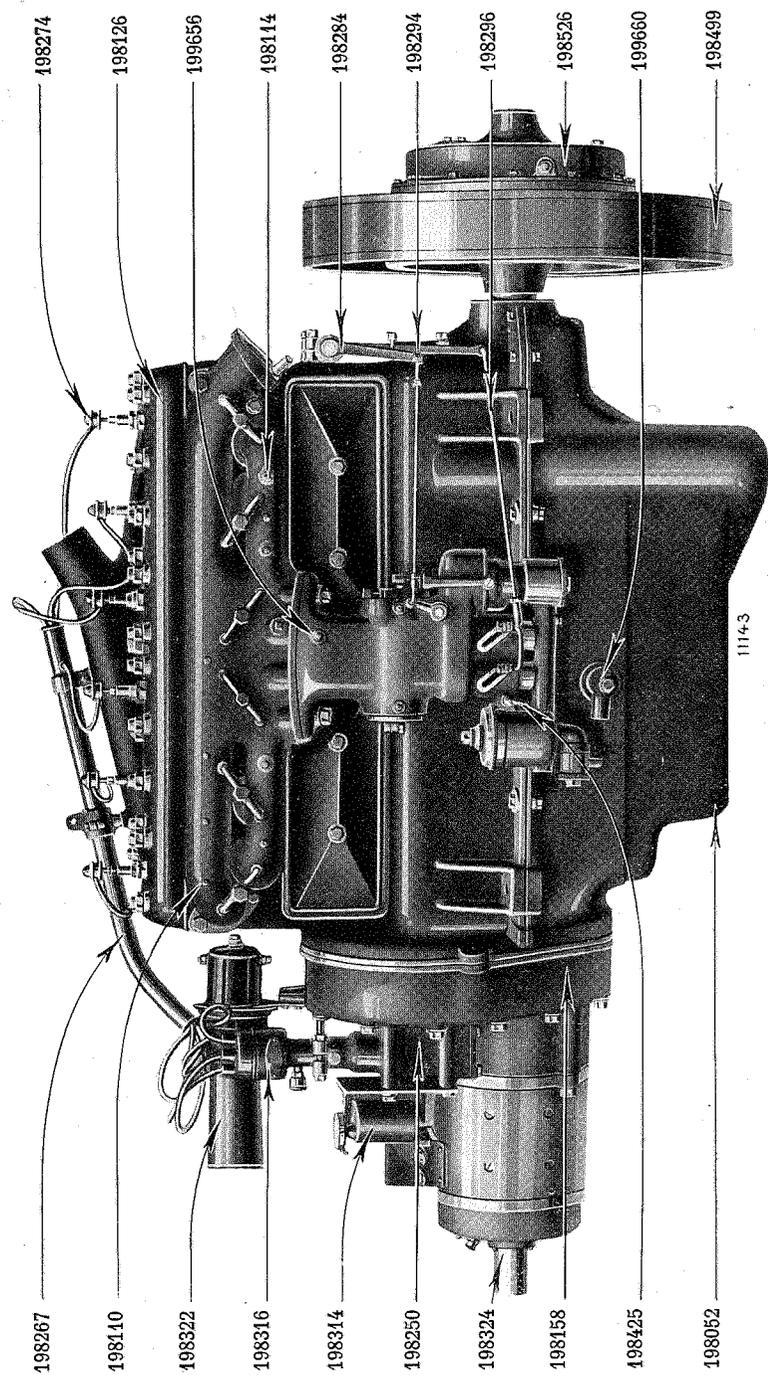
Le moteur. Vue extérieure, côté carburateur.
